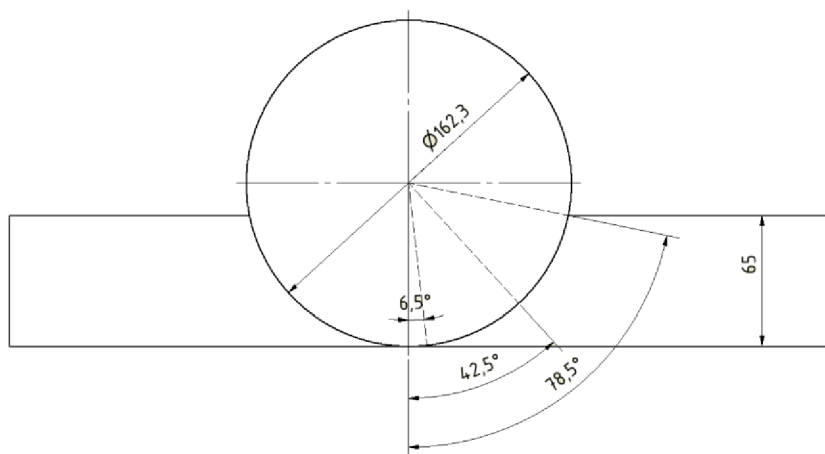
Fréza SECO R220.21-06.00-ON09-10 [26]
